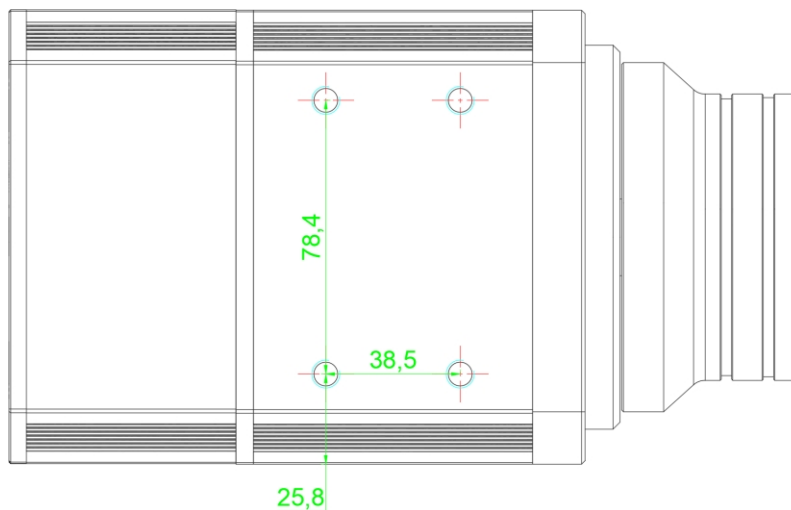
Befestigungsmuster für den VNM Wheelbase Premier.
